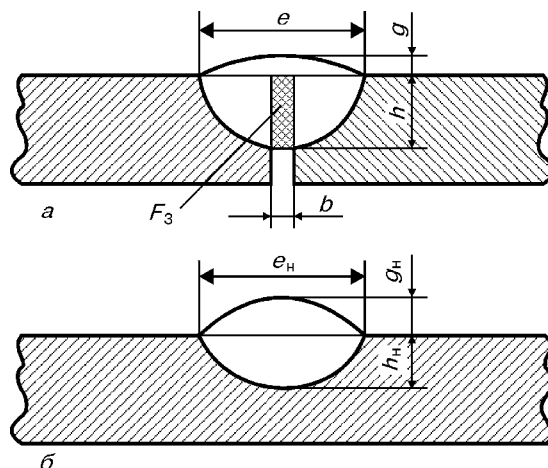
Размеры стыкового шва (а) и наплавленного валика (б)
